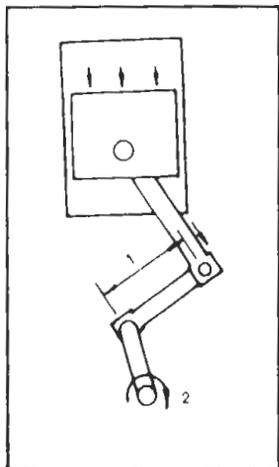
1.- Brazo de palanca. 2.- Par motor.
